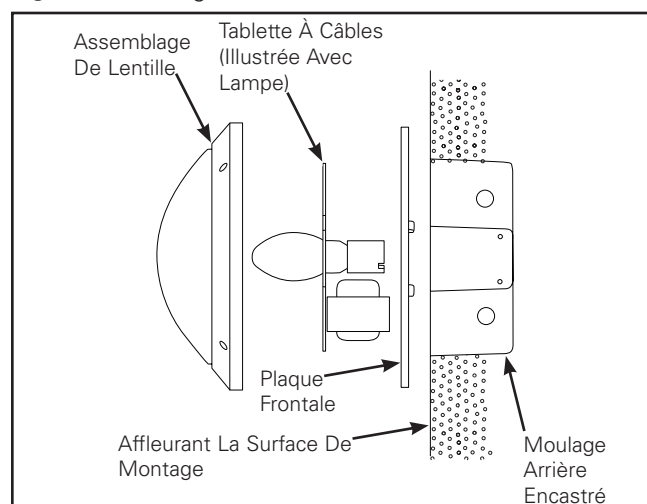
Assemblage lentille/plaque frontale pour modèles Harmony™
